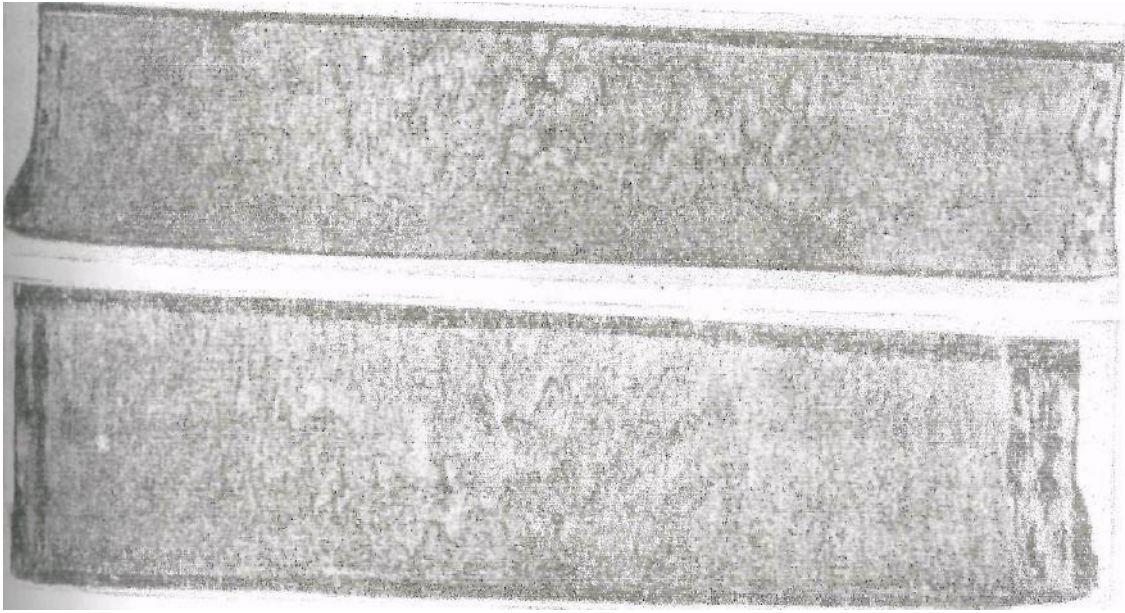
Злами шайб від заготовок з поверхневими рванинами.
